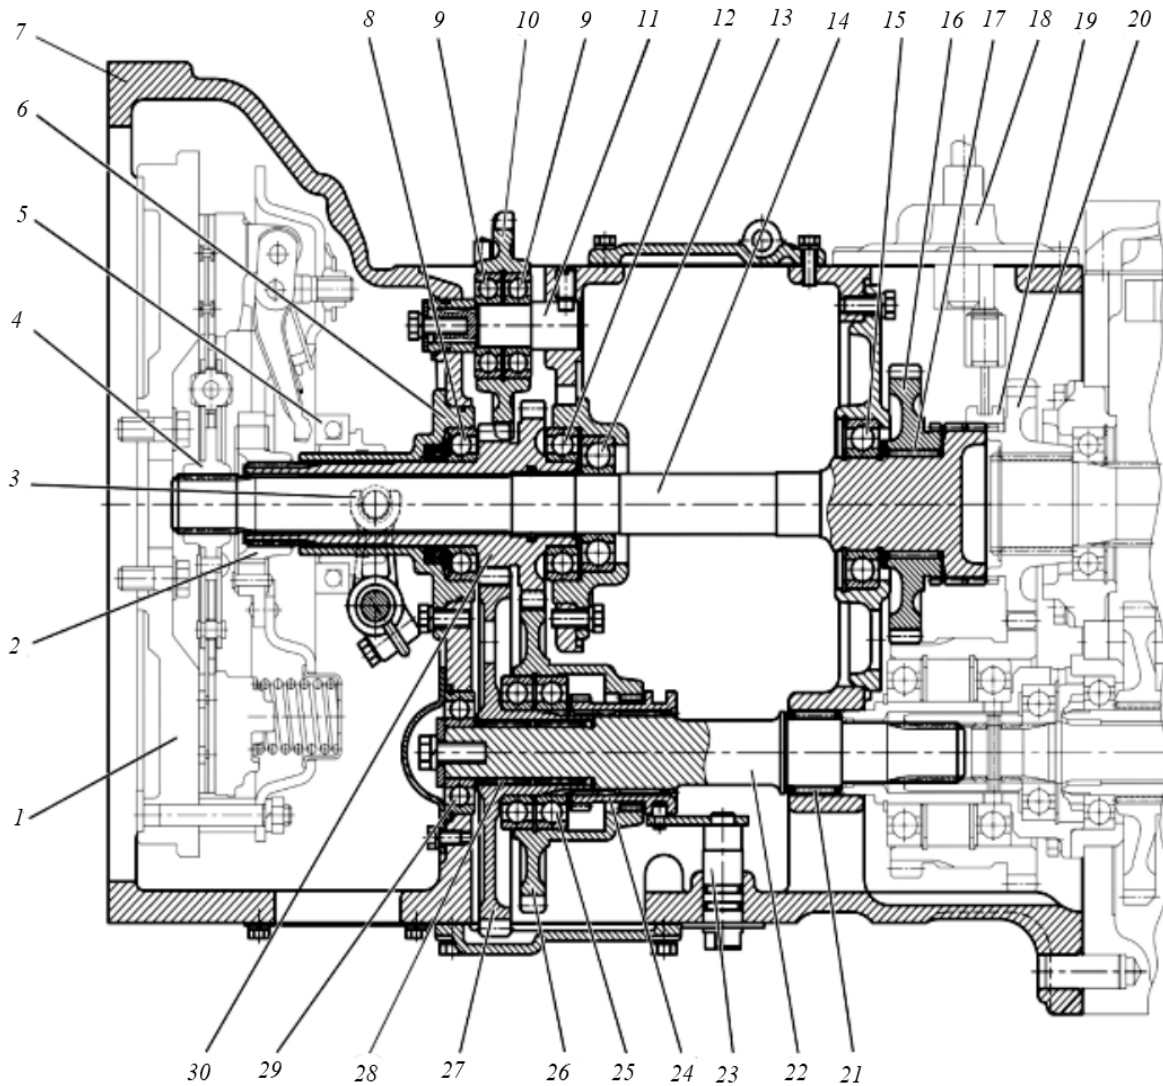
Корпус сцепления с понижающим механическим редуктором:
